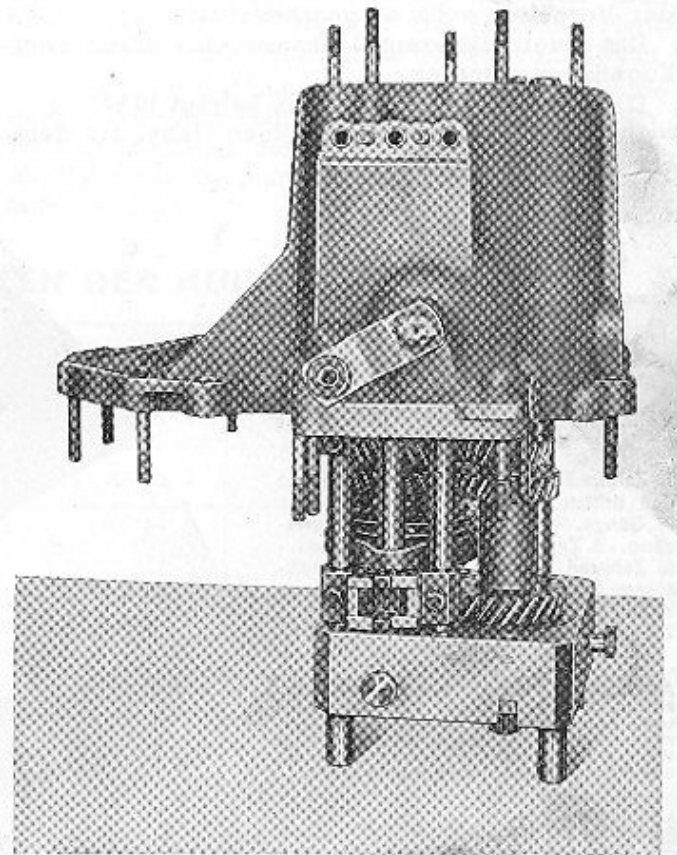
Montage des Getriebegehäuses auf das auf dem Werkzeug A. 70105 vormontierte Getriebe.
